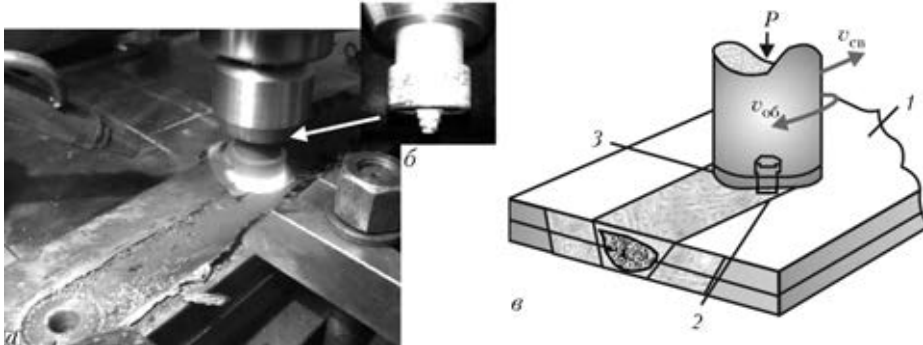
Общий вид установки (а), рабочий инструмент (б), схема процесса СТП (в): 1 — изделие; 2 — инструмент со специальным профилем; 3 — заплечик
